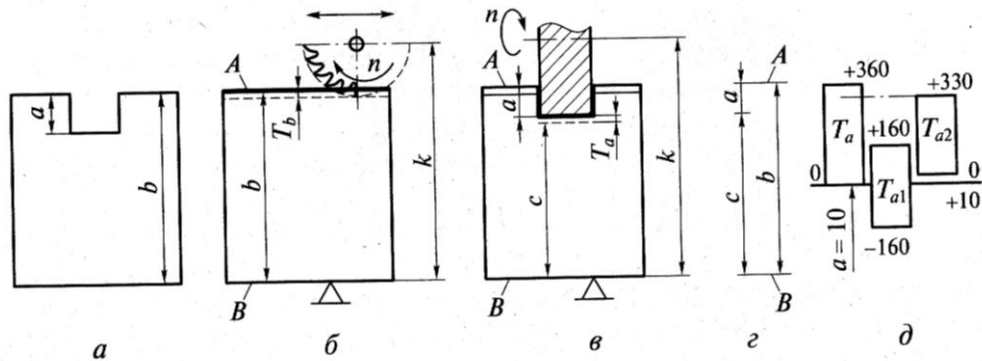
Послідовність обробки заготовки (а, б, в), її розмірний ланцюг (г), поля допусків (д)
